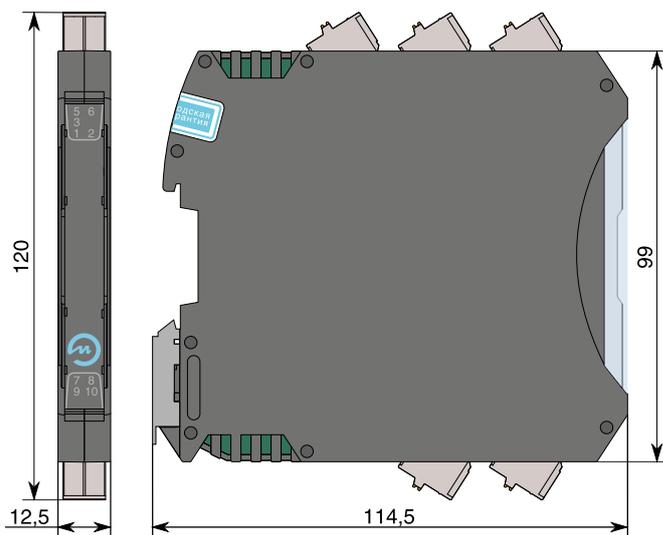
Габаритные размеры модуля в корпусе шириной 12,5 мм с разъемами с пружинными клеммниками и тестовыми гнездами
